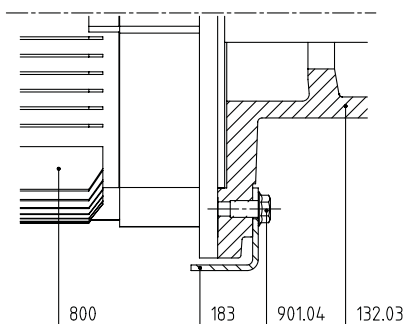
Befestigung Stützfuß bei Motor 160 und 180
